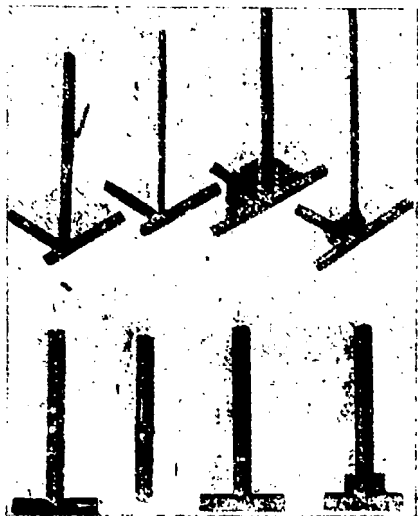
Т-образные и решетчатые трубчатые сварные соединения.
